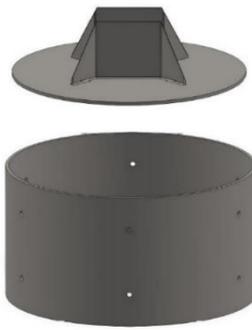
Acoplamiento del molde para crear el queso y el molde que usa la prensa.
